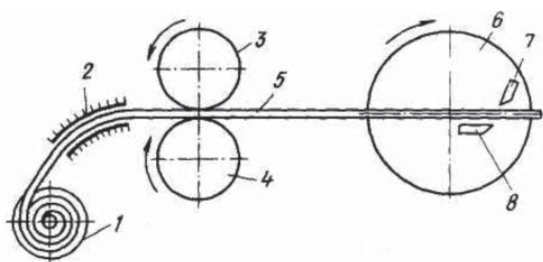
Схема станка для получения фибр из стальной проволоки: 1 – бухтодержатель; 2 – направляющая; 3 – прижимной валок; 4 – приводной валок; 5 – проволока; 6 – ротор; 7 – подвижный нож; 8 – неподвижный нож
